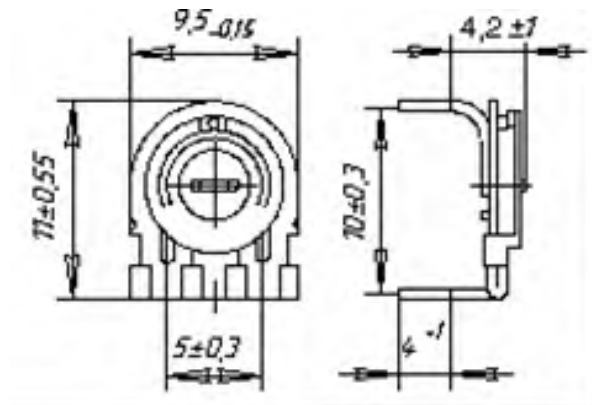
Габаритні розміри резистора типу СПЗ-386
